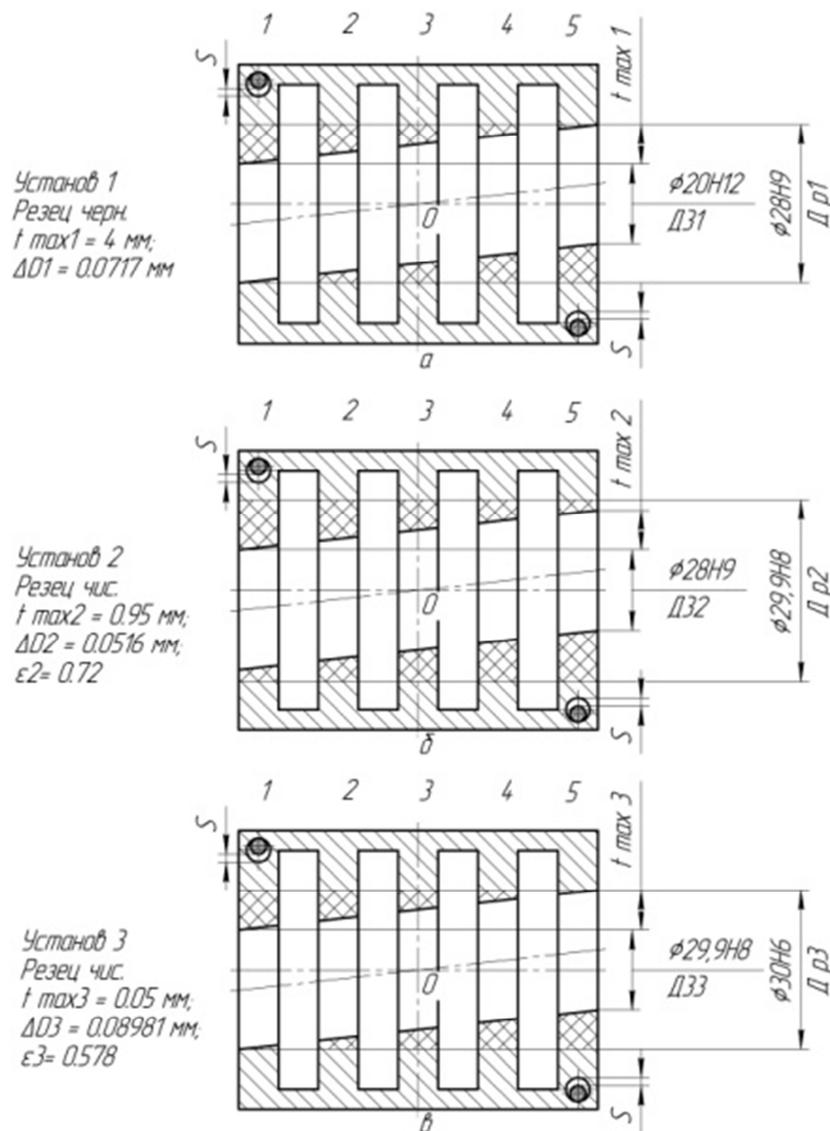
Схемы расположения припусков в заготовке при расточке с помощью многолезвовой борштанги: а – чернового; б – получистового; в – чистового;
